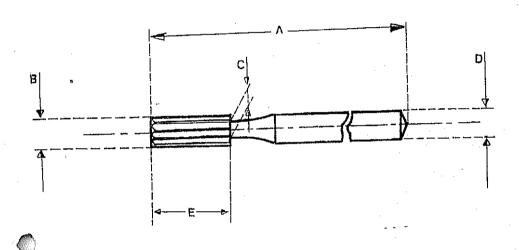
Fresas de carburo, forma cilindrica (claves: 060.431.0441, 000.431.0656, 060.431.0684)
